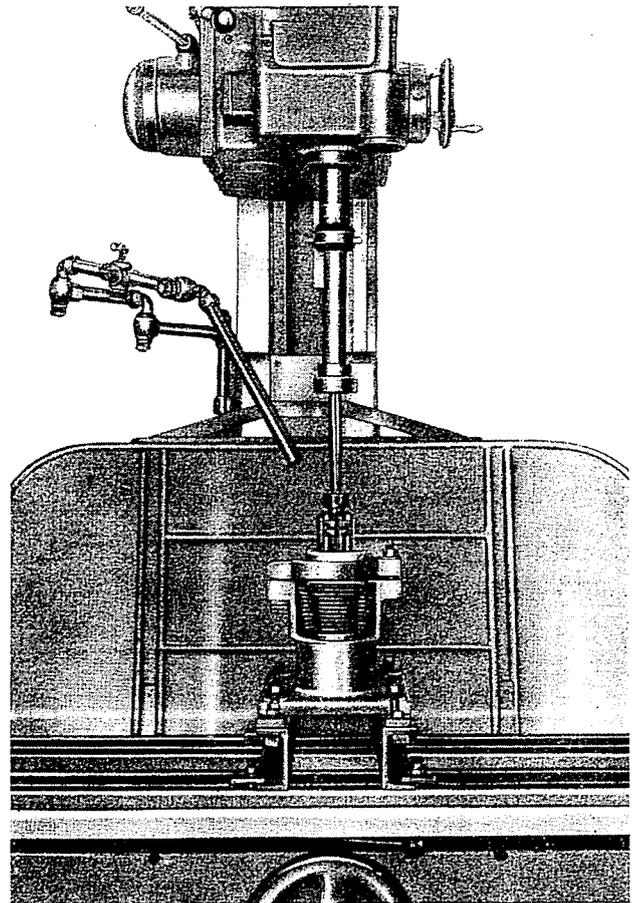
Honen eines mit Werkzeug A. 60000 auf der ortsfesten Ziehschleifmaschine aufgespannten Zylinders (Schleifmahle A. 11209).
